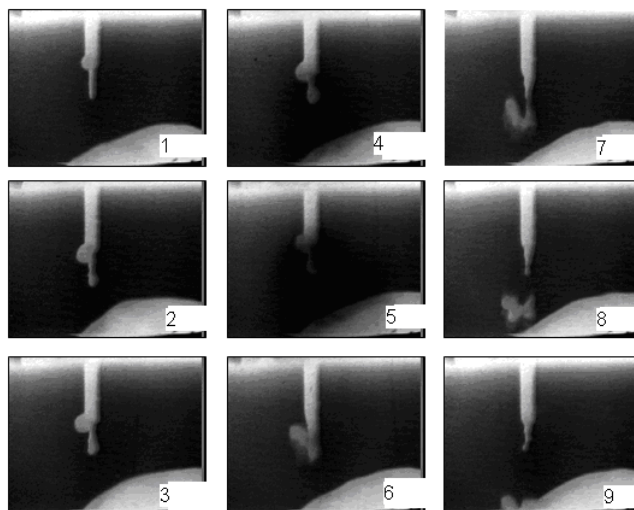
Кинокадры сварочного микроцикла адаптивного импульсного процесса сварки порошковой проволокой в смеси газов $Ar + CO_2$ с переносом металла без коротких замыканий дугового промежутка (последовательность кадров в пределах одного микроцикла 1 – 9)
